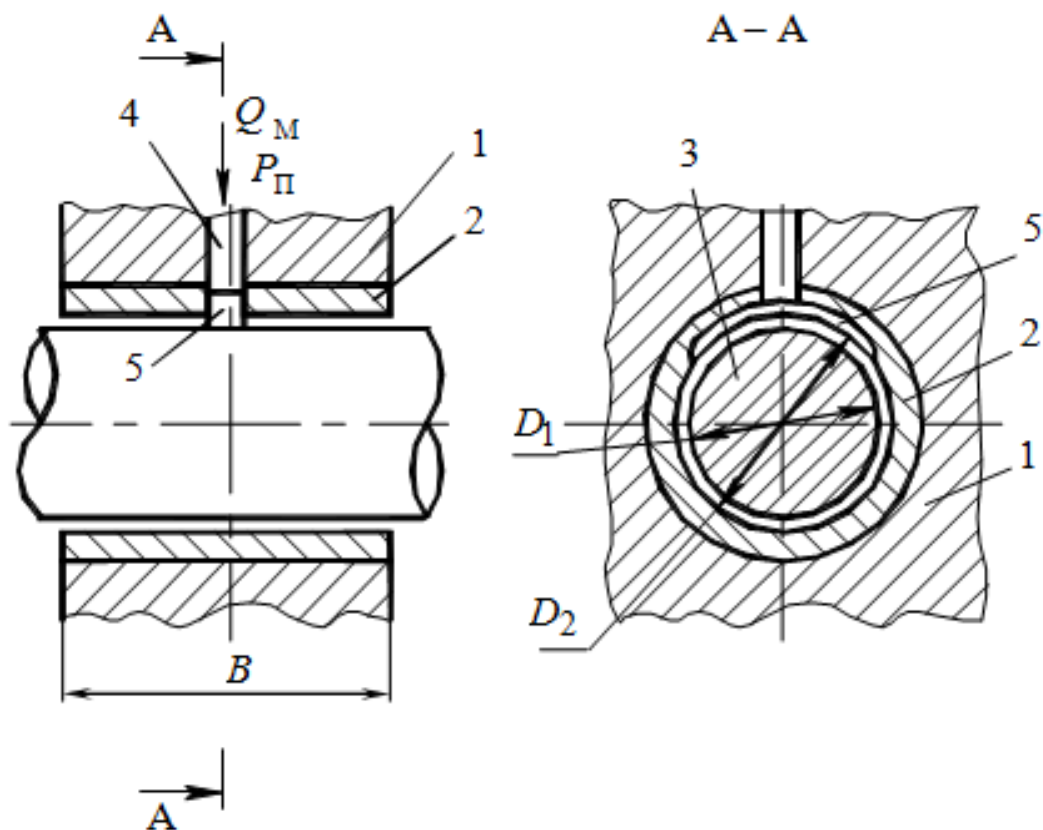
Основные геометрические размеры ГДО: 1 – разъемный корпус подшипника; 2 – сменный вкладыш с антифрикционным слоем; 3 – шип (вал); 4 – отверстие для подачи смазки под давлением  $p_{\Pi}$  и расходом  $Q_M$ ; 5 – маслораспределительная канавка или карман;  $B$  – ширина подшипника;  $D_2$  – диаметр подшипника;  $D_1$  – диаметр шипа
